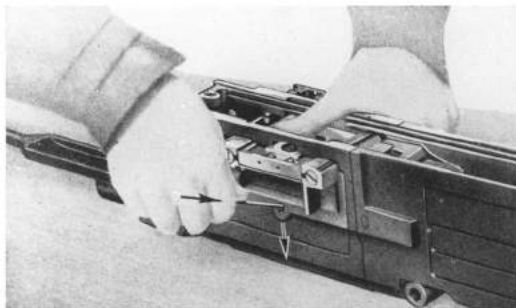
Teilweise Zerlegung der Waffe: Ausbau des Sperrrahmens zur Halterung des Zuführers
